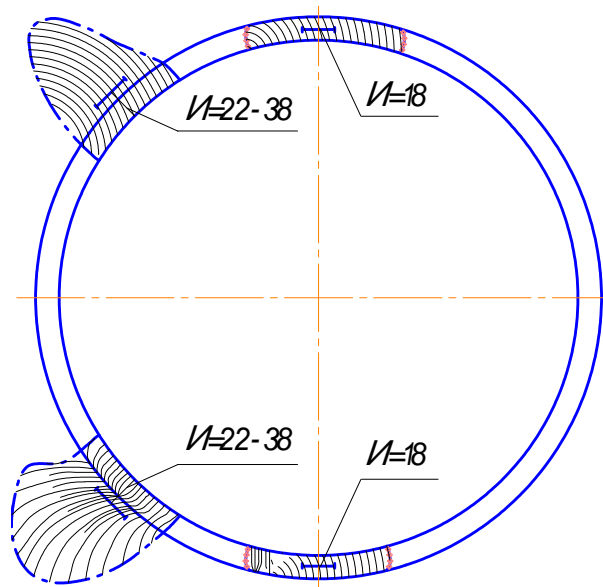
Картина трещин в хрупком покрытии, образовавшаяся на втором этапе испытаний по периметру сварного шва в месте приварки патрубка
